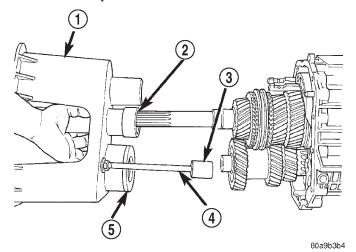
CONJUNTO DE HORMA DE ENSAMBLAJE
